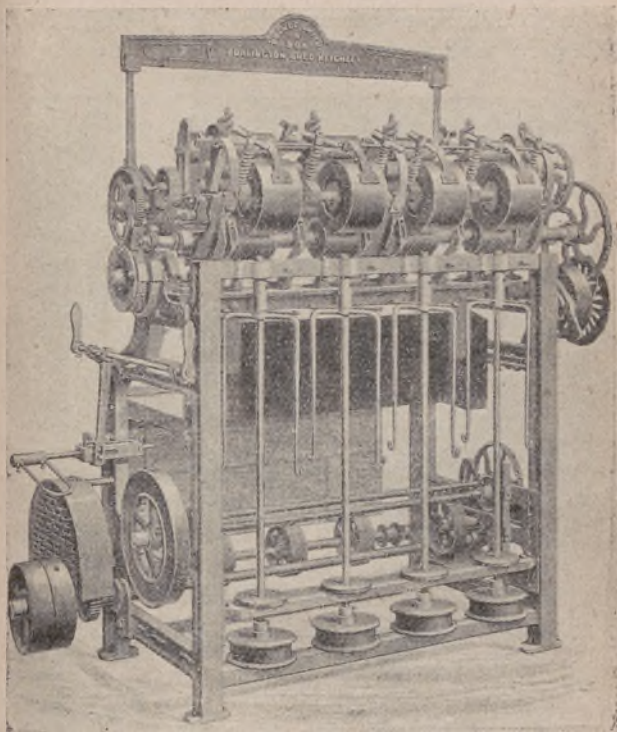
Stiratoio a 4 fusi (*4 Spindles Drawing box*).
